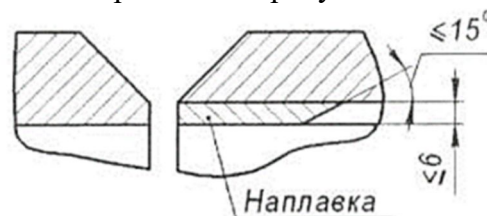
Наплавка внутренней поверхности трубы при стыковом соединении
